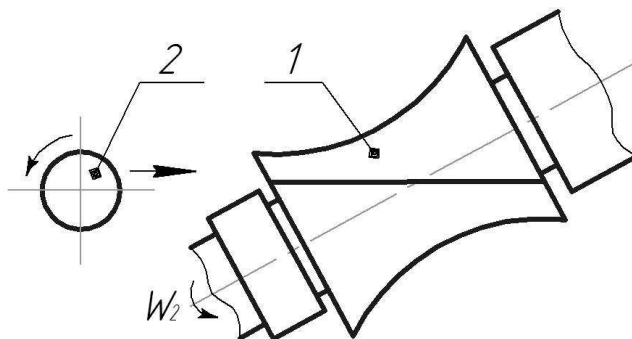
Схема изготовления гиперболических зубчатых колес
